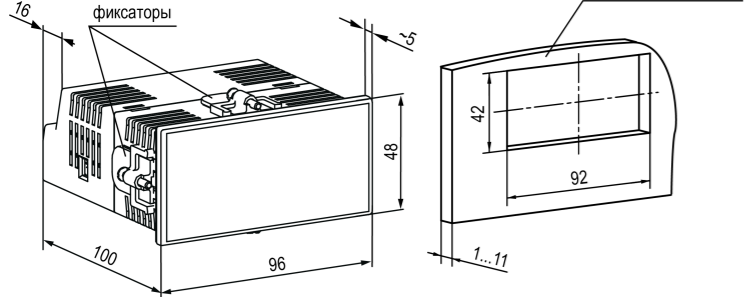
Габаритные размеры корпуса Щ2 и монтажного отверстия в щите
